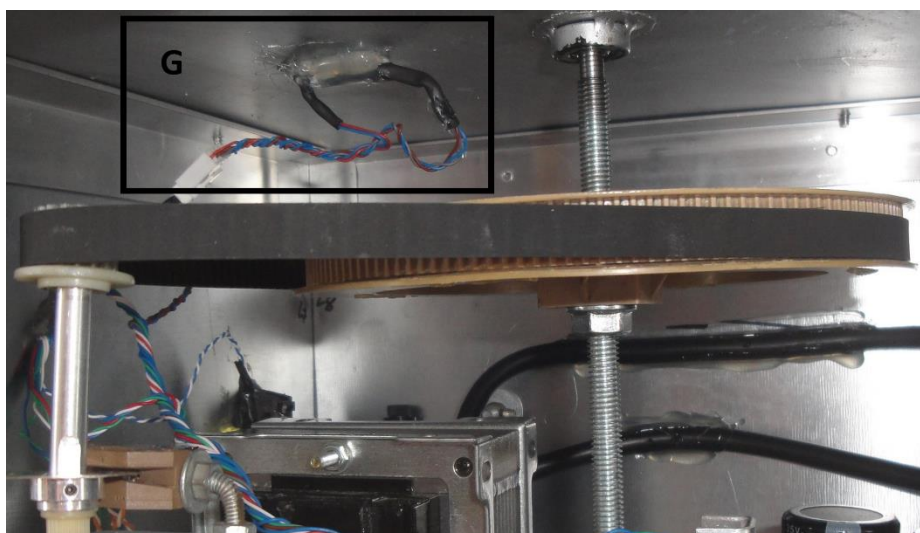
Pormenor do sistema de engrenagens e eixos do sistema mecânico
